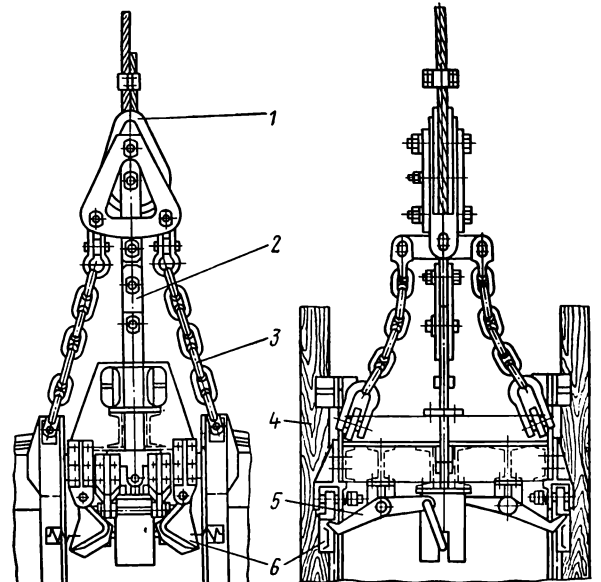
171. Общий вид парашюта для деревянных проводников с захватом конструкции МакНИИ:
